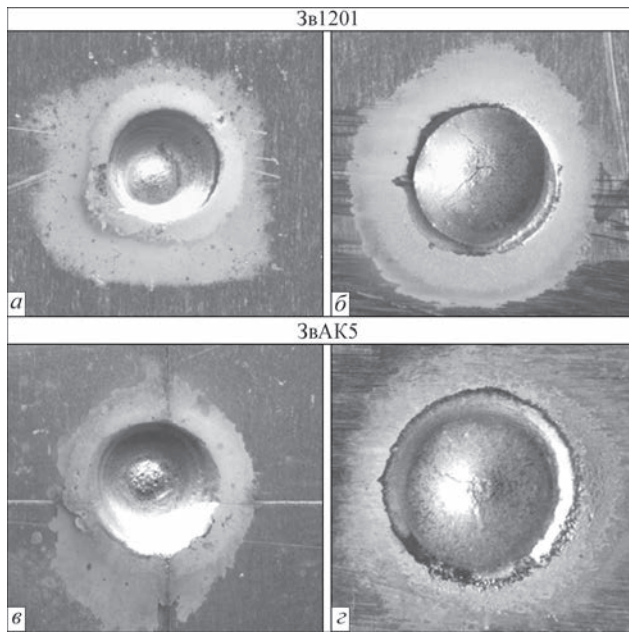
Зовнішній вигляд сплаву Д16Т після виконання технологічної проби «точковий шов» з присадками різного хімічного складу після ручного зварювання (а, б) та після повторного переплавлення (в, г)
